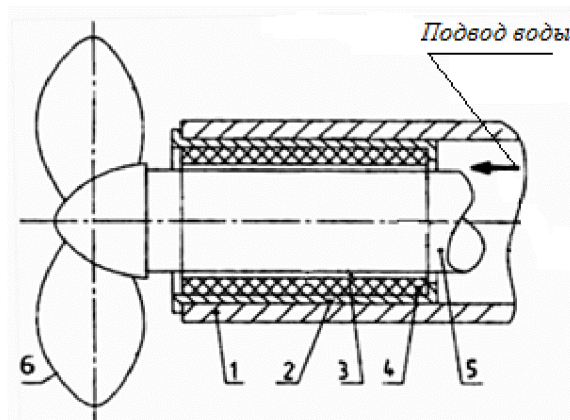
Дейдвудное устройство с подшипником из капролона со смазкой и охлаждением водой: 1 – дейдвудная труба; 2 – втулка; 3 – смазывающая канавка; 4 – подшипник из капролона; 5 – вал; 6 – гребной винт
